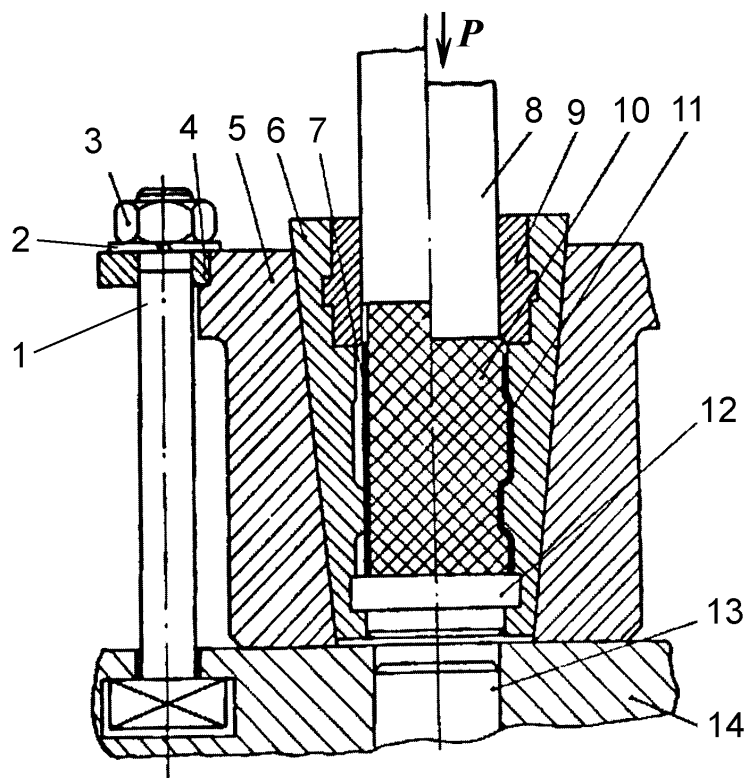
Схема штампа для роздавання трубчастих заготовок еластичним середовищем: 1 – стяжний болт; 2 – шайба; 3 – гайка; 4 – притискне кільце; 5 – контейнер; 6 – рознімна матриця; 7 – заготовка; 8 – пуансон; 9 – напрямне кільце; 10 – поліуретанова вкладка (еластичне середовище); 11 – деталь; 12 – заглушка; 13 – виштовхувач; 14 – стіл преса
